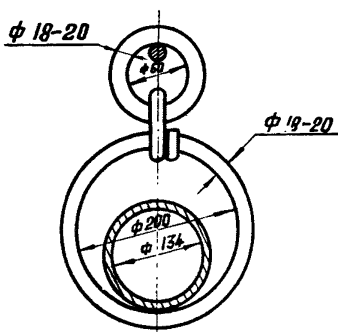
Конструкция подвески выдвижной предохранительной крепи
